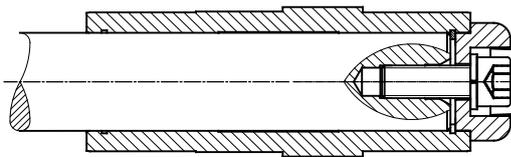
Getriebe auf Welle ohne Anlageschulter mit Befestigungselement befestigt
